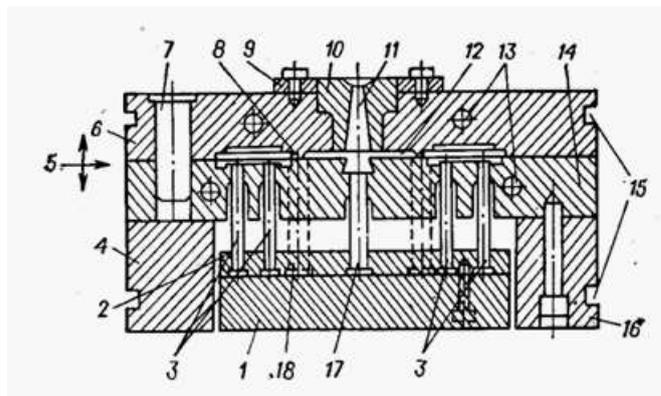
Термопластавтомат - агрегат для изготовления изделий методом литья под давлением
